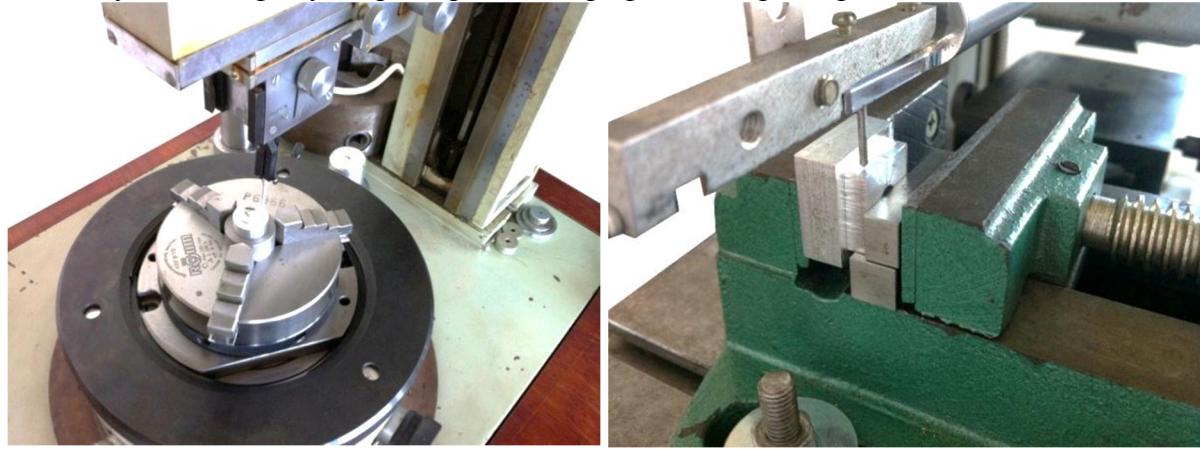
Процес вимірювання оброблених деталей: а – на кругломірі; б – на профілометрі
